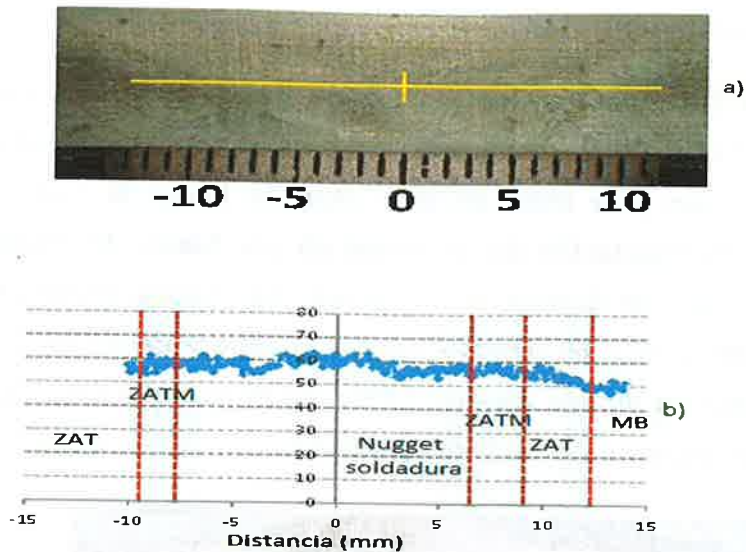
Perfil de microdureza de la union soldada FSW.
